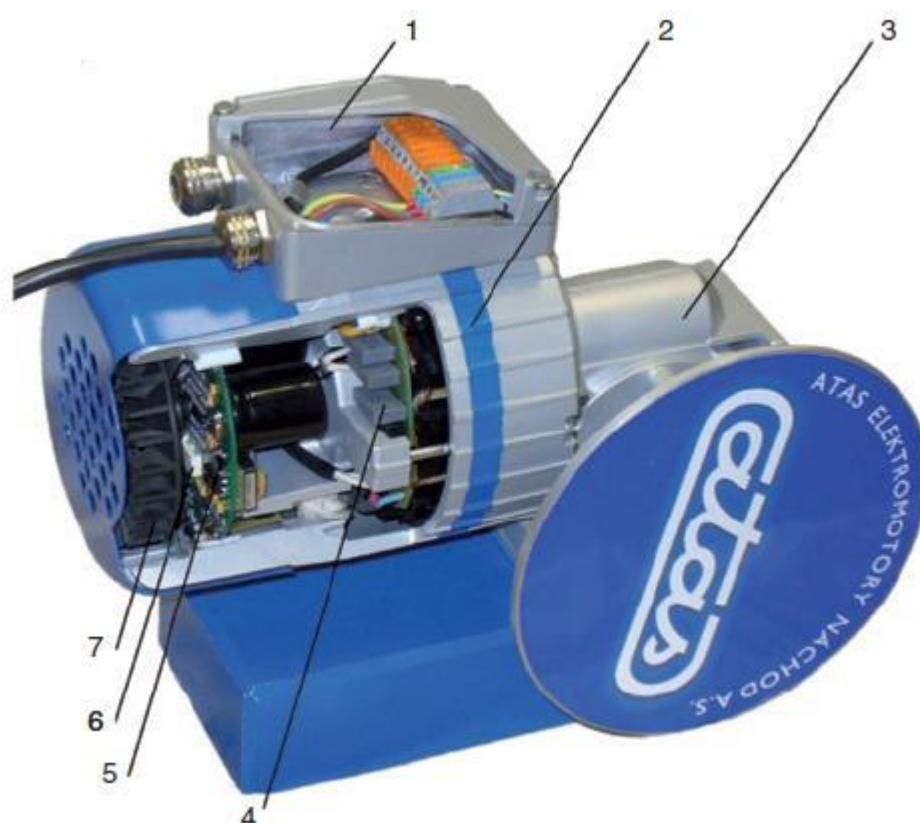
1-kostra statoru, 2-magnety, 3-rotorový svazek, 4-komutátor, 5-kartáč(uhlík), 6-držák kartáčků, 7-chladicí ventilátor elektromotoru
